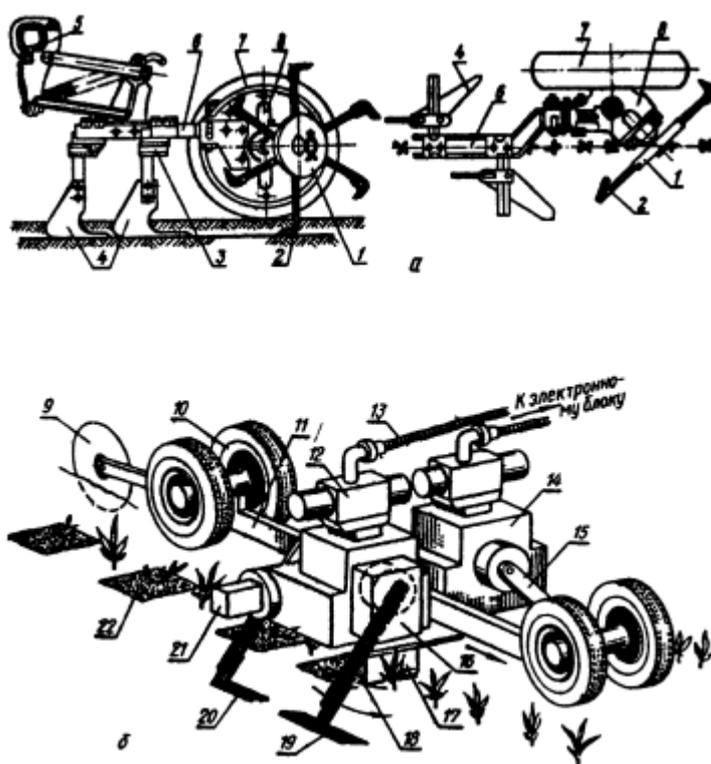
Прореживатели: а - секция прореживателя УСМП - 5,4; б - секция прореживателя ПСА - 2,7; 1 - режущая головка; 2,19 и 20 - ножи; 3 - держатель; 4 - односторонние лапы; 5 - брус - рама; 6 - грядиль; 7 и 10 - колеса; 8 - корпус редуктора; 9 - диск - заземлитель; 11 - рамка; 12 - гидрораспределитель; 13 - кабель; 14 - привод; 15 и 18 - рычаги; 16 и 17 - датчики; 21 - брус; 22 - вырез
